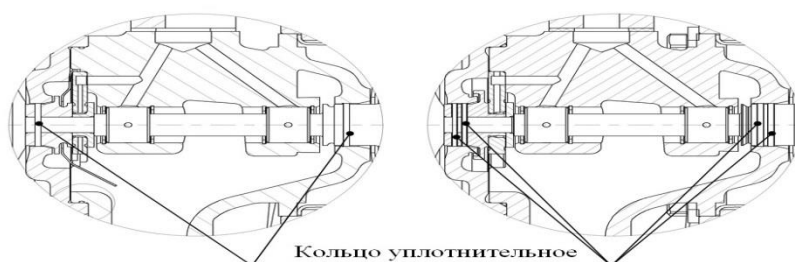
Схема установки колец уплотнительных на роторе турбокомпрессора
